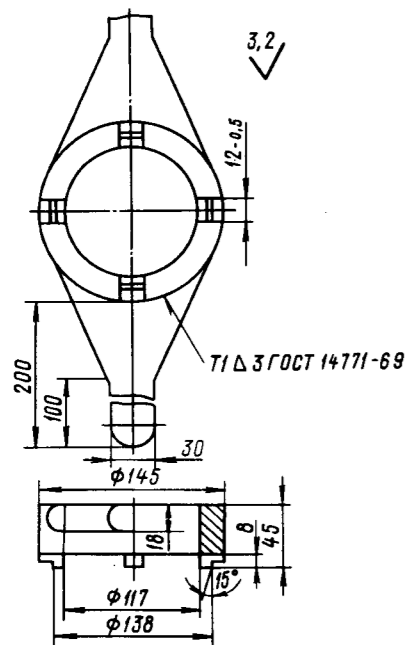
Ключ для монтажа круглой гайки гидроцилиндров II типа
